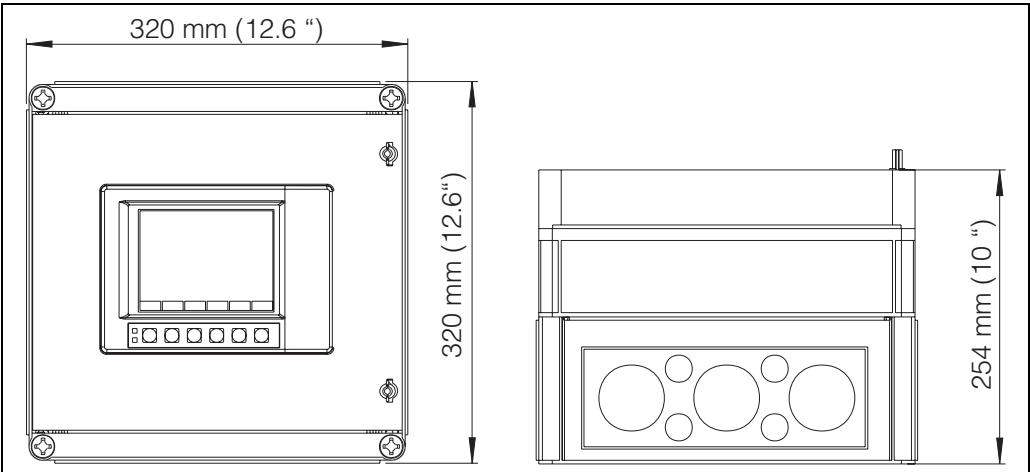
Dimensions boîtier de terrain (indications en mm)
